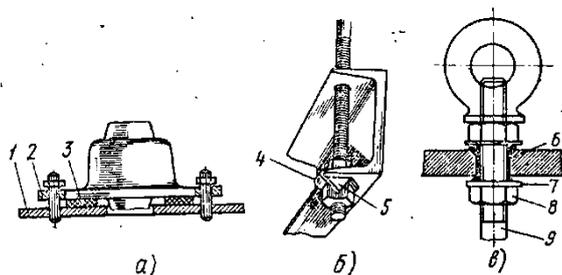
Способы выполнения отдельных операций сборки: а — установка, резиновой прокладки под фланец ввода, б — установка шайбы для предотвращения самоотвинчивания гайки на нижнем конце подъемной шпильки, в — уплотнение верхнего конца подъемной шпильки в месте прохода через крышку трансформатора; 1 — крышка трансформатора, 2 — фланец ввода, 3 — прокладка из маслостойкой резины 4 — загиб фасонной шайбы на ярмовую балку, 5 — загиб уголка шайбы на грань гайки, 6 —уплотнение из асбестового шнура, пропитанного лаком ГФ-95, 7—стальная шайба, 8 — гайка, 9 - подъемная шпилька
